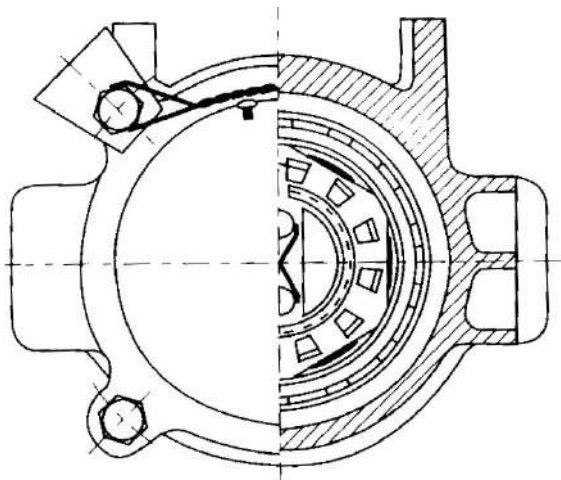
Буксовий вузол, що має корпус з прямокутними приливами
